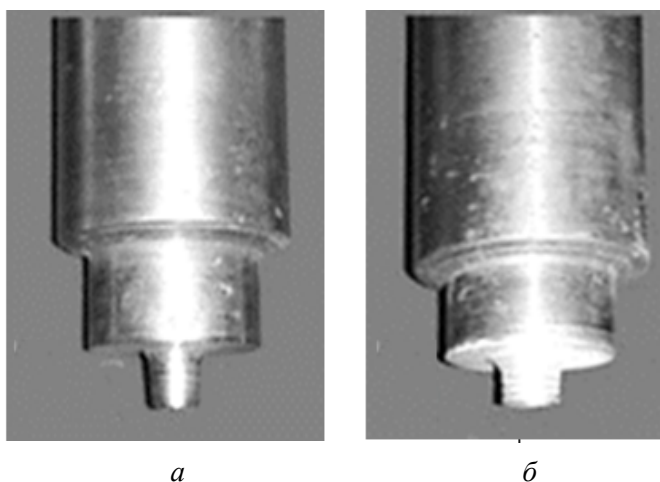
Геометрия наконечника сварочного инструмента:
